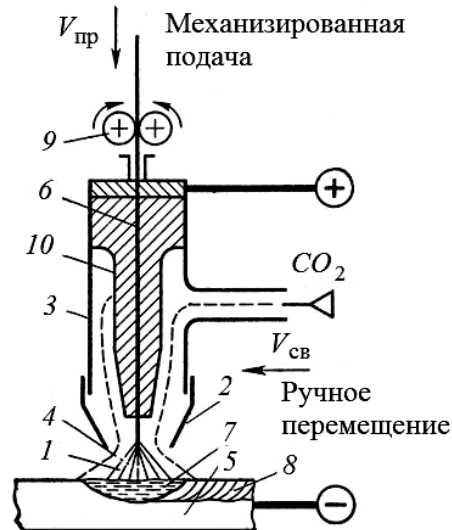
Схема процесса дуговой сварки в углекислом газе
